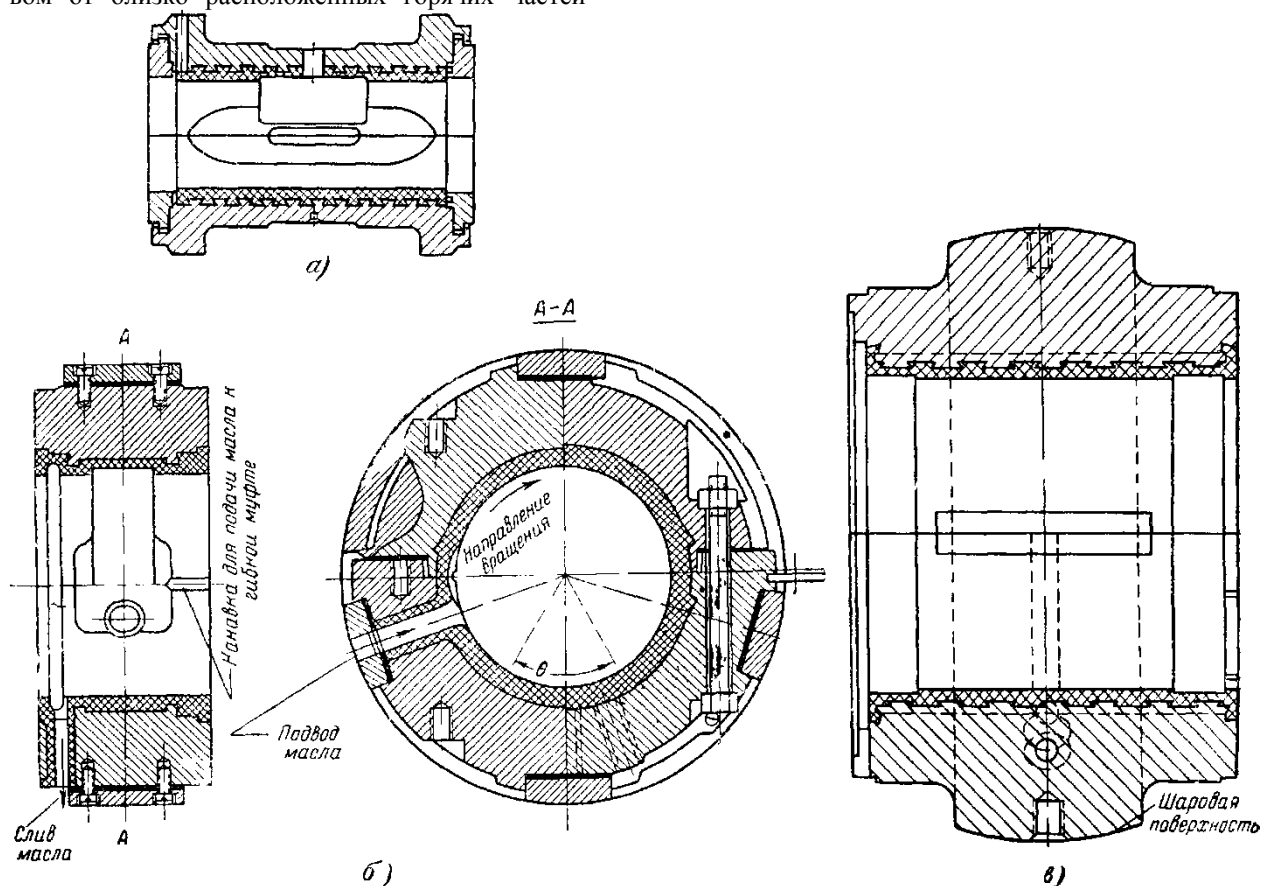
Типы опорных подшипников. а—жесткий цилиндрический нерегулируемый опорный подшипник; б—цилиндрический регулируемый подшипник, в—самоустанавливающийся шаровой опорный подшипник.
